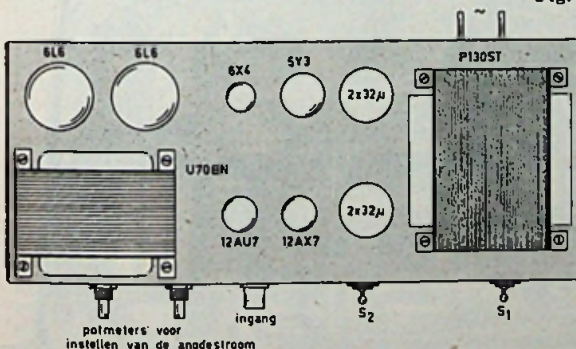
OPSTELLINGSPLAN VOOR HET BOVEN-AANZICHT VAN DE HOOFDVERSTERKER
